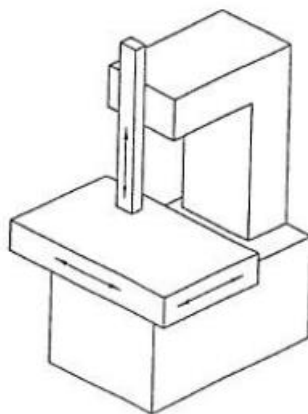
Výložníkový CMM s pohyblivým portálem [32]
